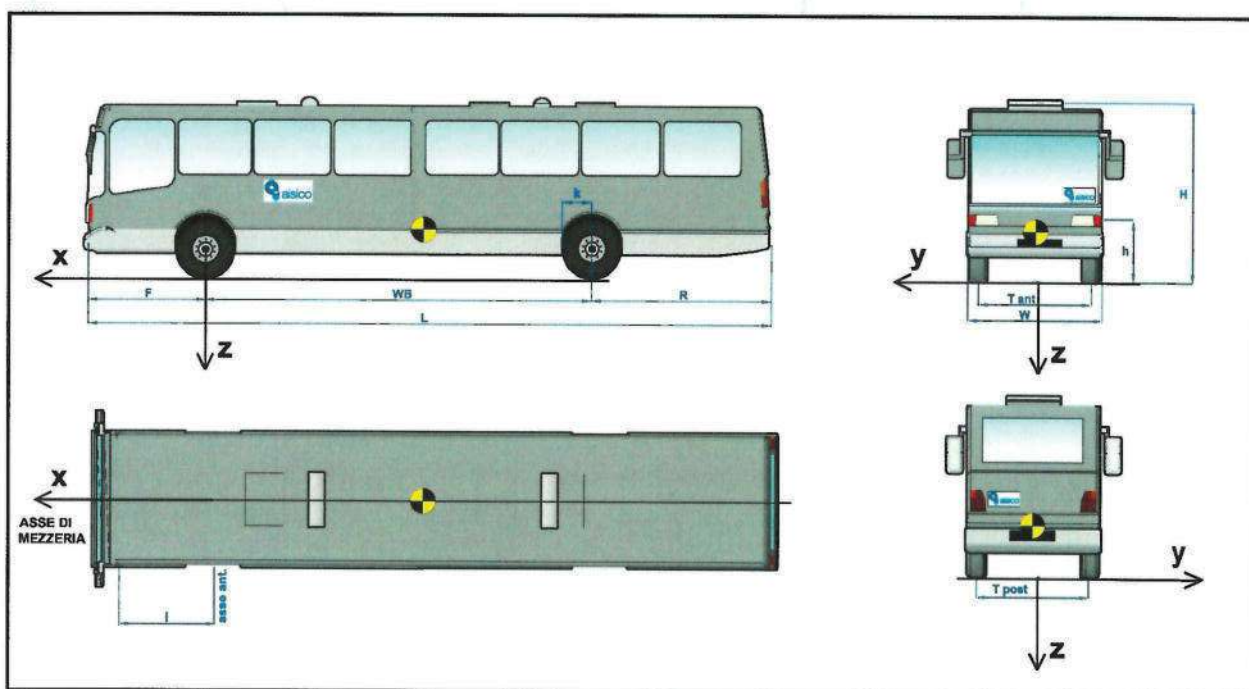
Figure 3 Dimensioni del veicolo – Vehicle dimensions
